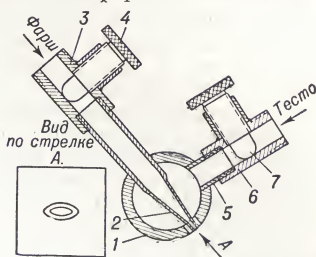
Формующее устройство автомата: 1 — корпус формующего устройства; 2 — фаршевая трубка; 3 — корпус регулятора фарша; 4 — регулирующий винт; 5 — тестовая трубка; 6 — корпус регулятора теста; 7 — регулировочный винт.
